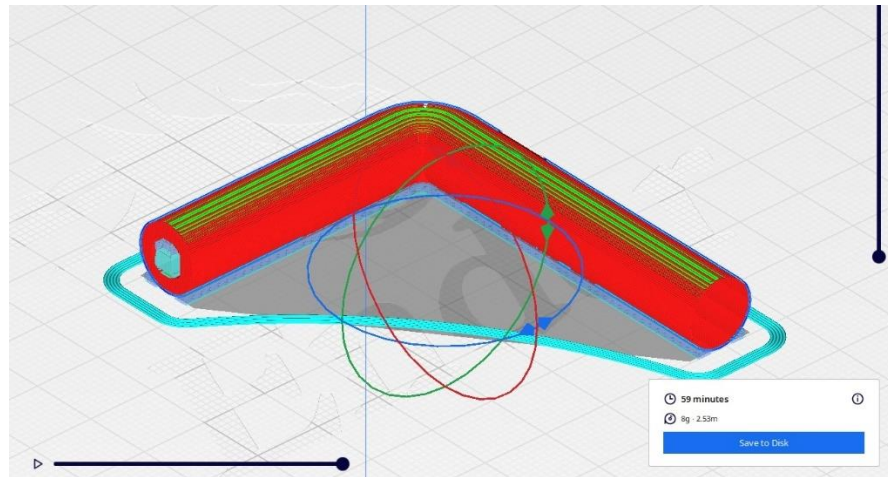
Hasil Pemesinan CNC Bagian 2
